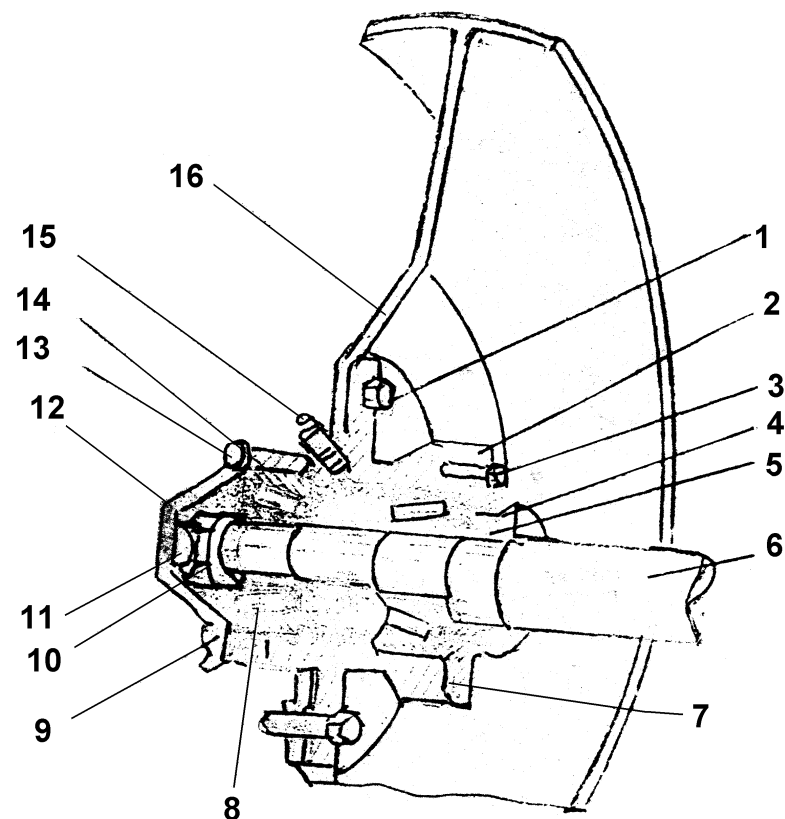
Колесо ПВШ 36.000-02, ПКГ 09.000-01
